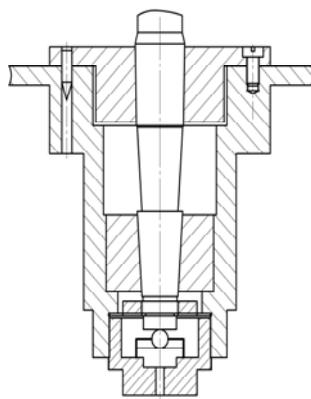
Конические вертикальные направляющие с саморазгружающимися устройствами
